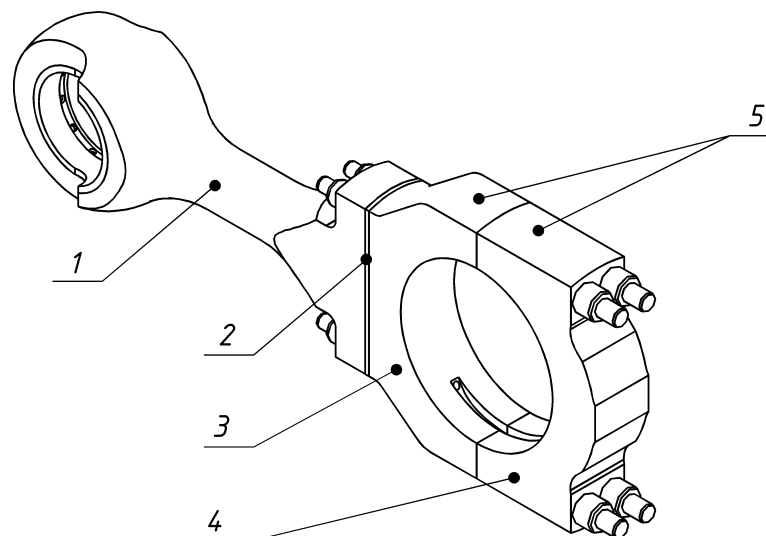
Шатун дизеля 9ЧН 32/40. 1 – стрижень шатуна з верхньою голівкою; 2 – прокладка для регулювання ступеню стиску; 3 – верхня частина корпусу шатунного підшипника; 4 – нижня частина корпусу шатунного підшипника; 5 – корпус шатунного підшипника
